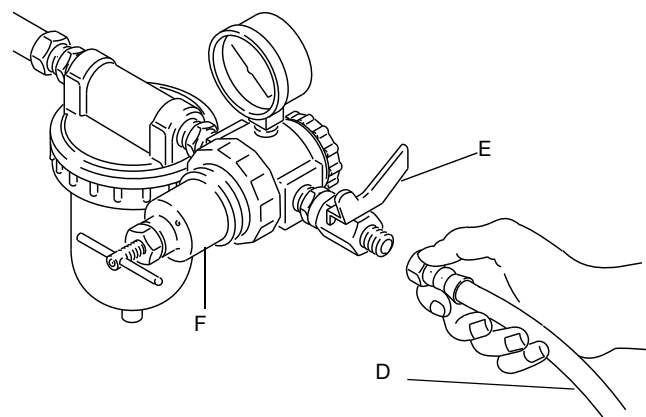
Flexible pneumatique du pistolet Installation typique
